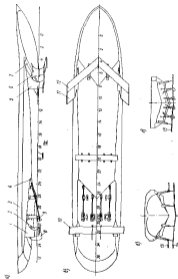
Схема гидродинамического устройства и компоновки частей теплохода «Спутник»: а — вид сбоку; б — вид на левый борт; в — вид на правый борт; г — вид на корму.
